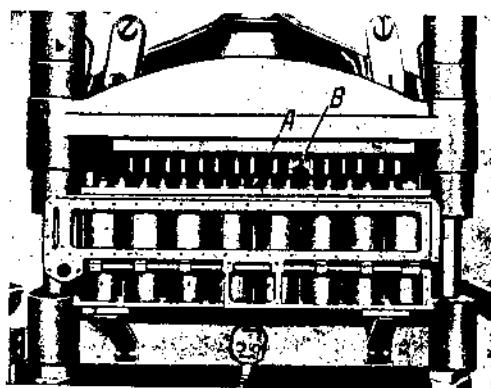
Приспособление для запрессовки втулок (к рис. 372).
